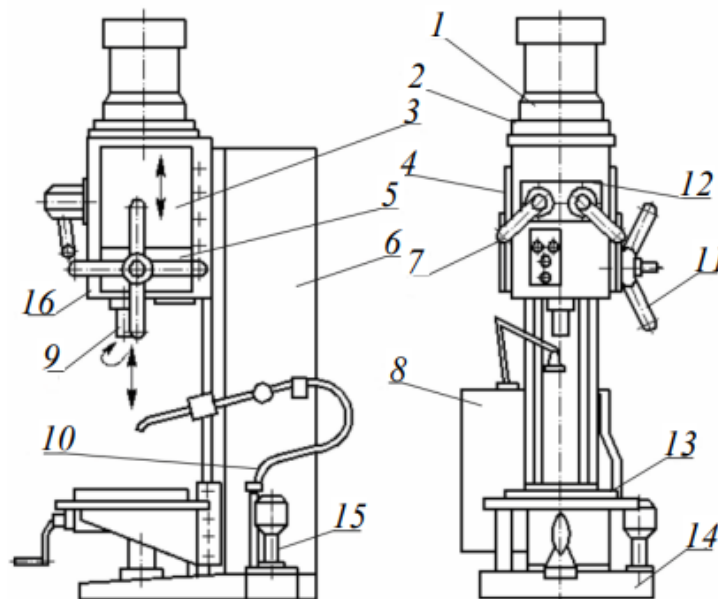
Схема вертикально-свердлувального верстата:
